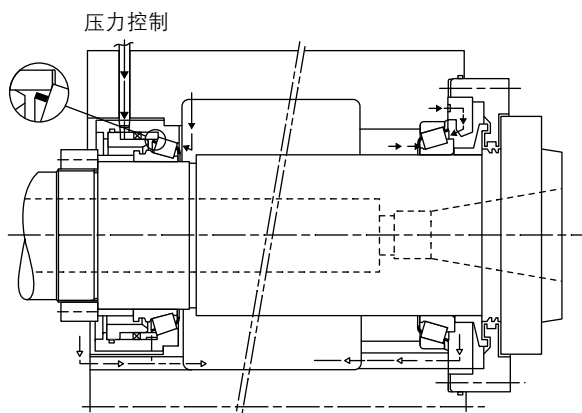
采用Hydra-Rib 轴承（有轴向进油冷却）和TS 轴承（在滚子两端都有喷油孔用于进油和冷却）的简易安装
